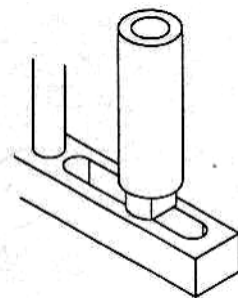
Натяжка V-ремня (фрезерная обработка)
